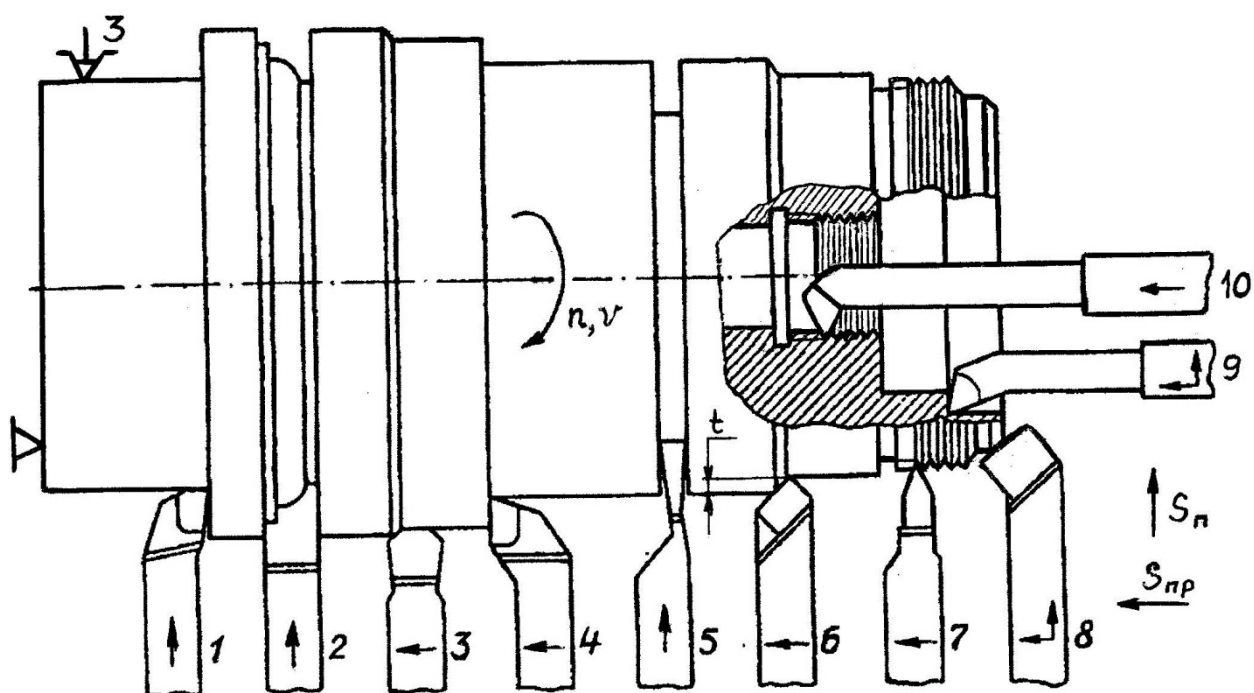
Основные типы токарных резцов и их относительные движения (подачи) при обработке различных поверхностей на заготовке, установленной в трехкулачковом патроне: 1 – подрезной левый; 2 – фасонный; 3 – проходной широкий для чистовой обработки правый; 4 – проходной упорный правый; 5 – прорезной (отрезной); 6, 8 – проходные упорные (фасочные) правые; 7, 10 – резьбовые для нарезания наружной и внутренней резьб; 9 – расточной; по форме режущей части – 1, 4, 8, 9, 10 – отогнутые; 3, 6 – прямые; 5, 7 – оттянутые; 1, 4, 8, 9, 10 – изогнутые.
